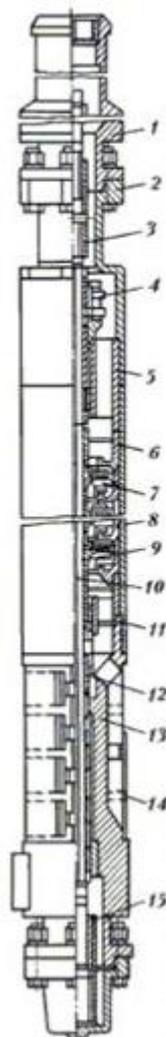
Погружной центробежный насос: 1 – секция верхняя с ловильной головкой; 2 – секция нижняя; 3 – муфта шлицевая; 4 – пята опорная; 5 – корпус подшипника; 6 – аппарат направляющий; 7 – колесо рабочее; 8 – корпус; 9 – вал; 10 – шпонка; 11 – подшипник скольжения; 12 – втулка защитная; 13 – основание; 14 – сетка фильтра; 15 – муфта приводная.
